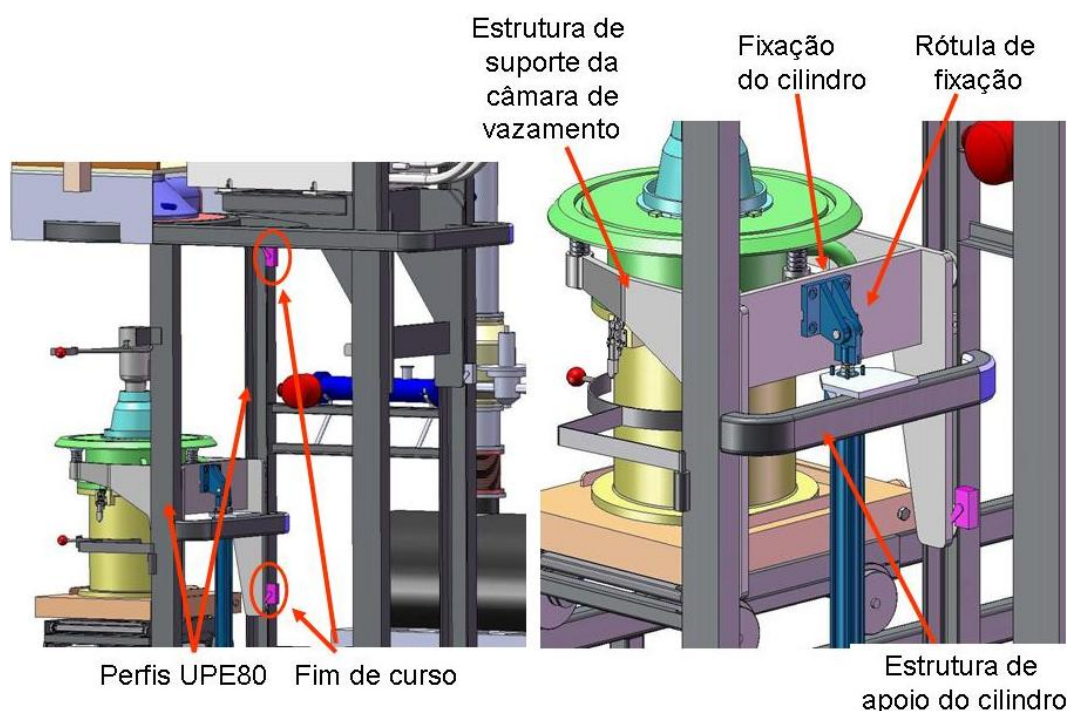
Vista geral da fixação do cilindro hidráulico ao sistema da câmara de vazamento. Vista em pormenor das fixações do corpo e da haste do cilindro.
